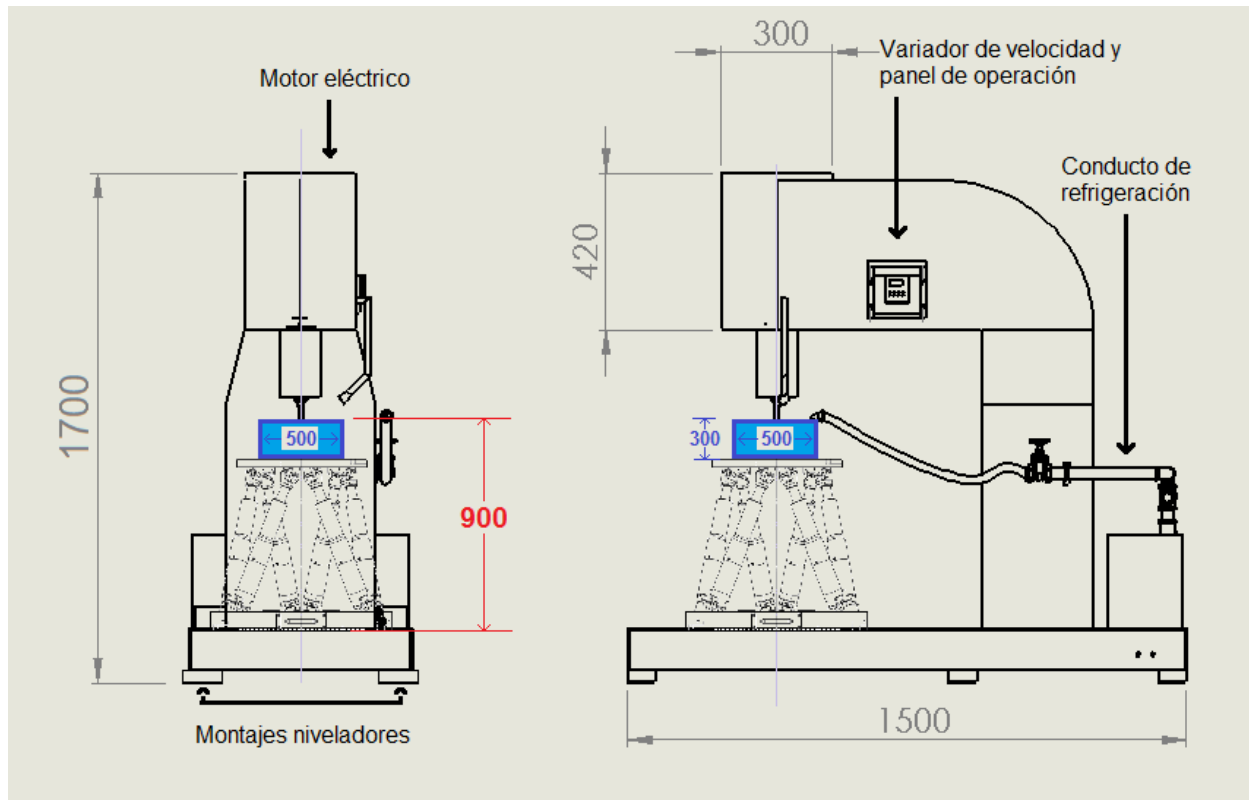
Dimensionamiento básico de la fresadora con componentes principales
